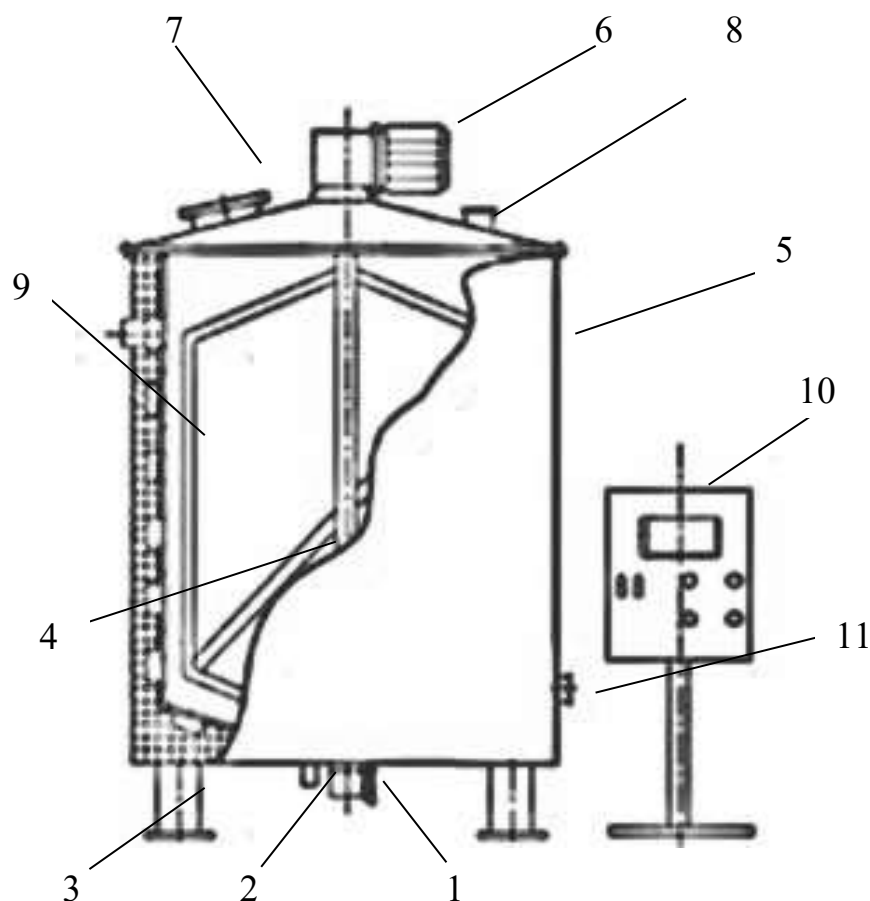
Общий вид резервуара марки В2-0КВ-10:
